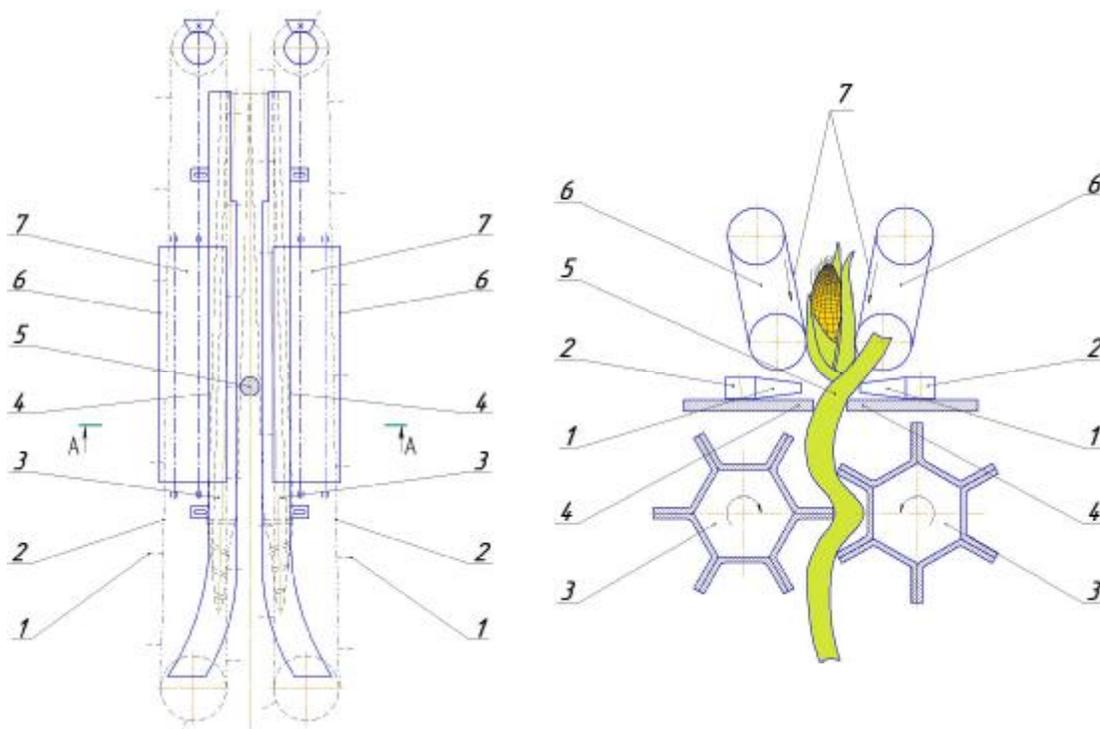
Початкоотделяющий аппарат: а – вид сверху; б – разрез А-А: 1 – лапки; 2 – подающие цепи; 3 – протягивающие вальцы; 4 – пластины; 5 – стебель; 6 – транспортеры; 7 – рабочая поверхность транспортеров
